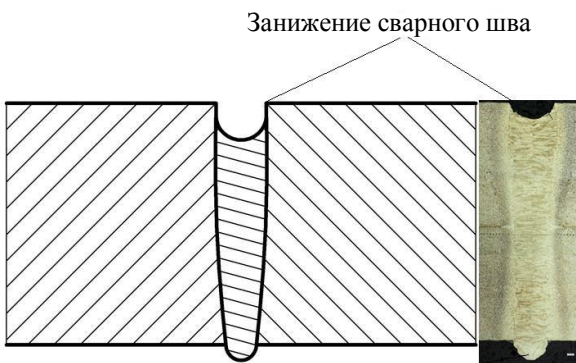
Дефект лазерной сварки с глубоким проплавлением – занижение сварного шва
